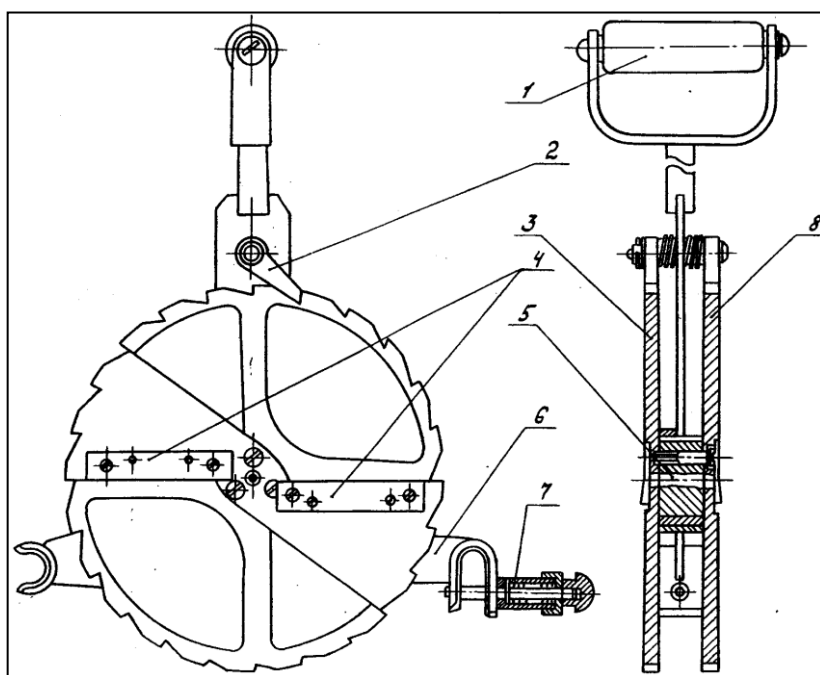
Торцовочное устройство: 1 – рукоятка; 2 – собачка; 3, 8 – колёса храповые; 4 – ножи; 5 – ось; 6 – основание; 7 – фиксатор
